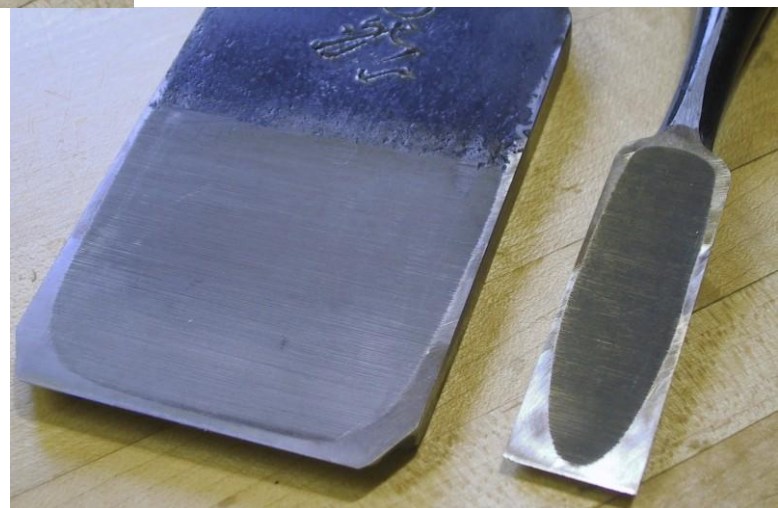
Fer Shizen et ciseau Matsumura vus du dessous. La dépression ne laisse qu'une mince bande de métal très dur sur la planche et facilite d'autant l'aplanissement de la planche.
